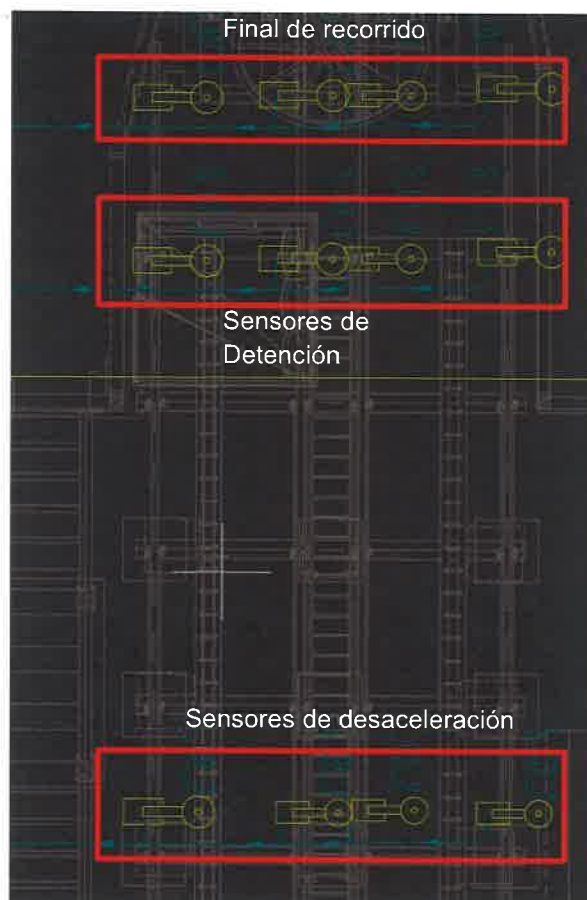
Parte superior del plano de rodadura. Izquierda: cabina 1 y derecha cabina 2
